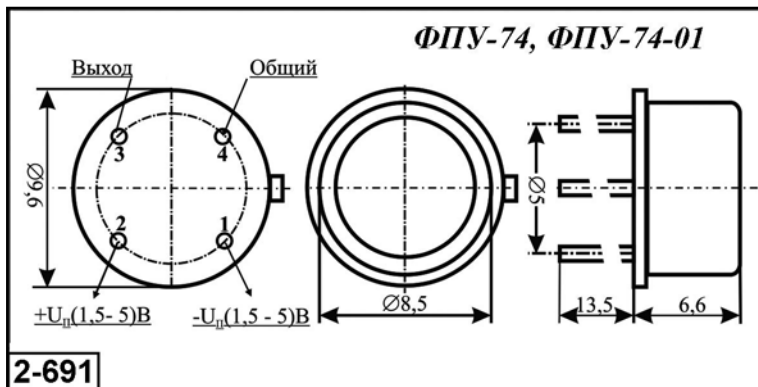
Внешний вид и габаритные размеры ФПУ-74
